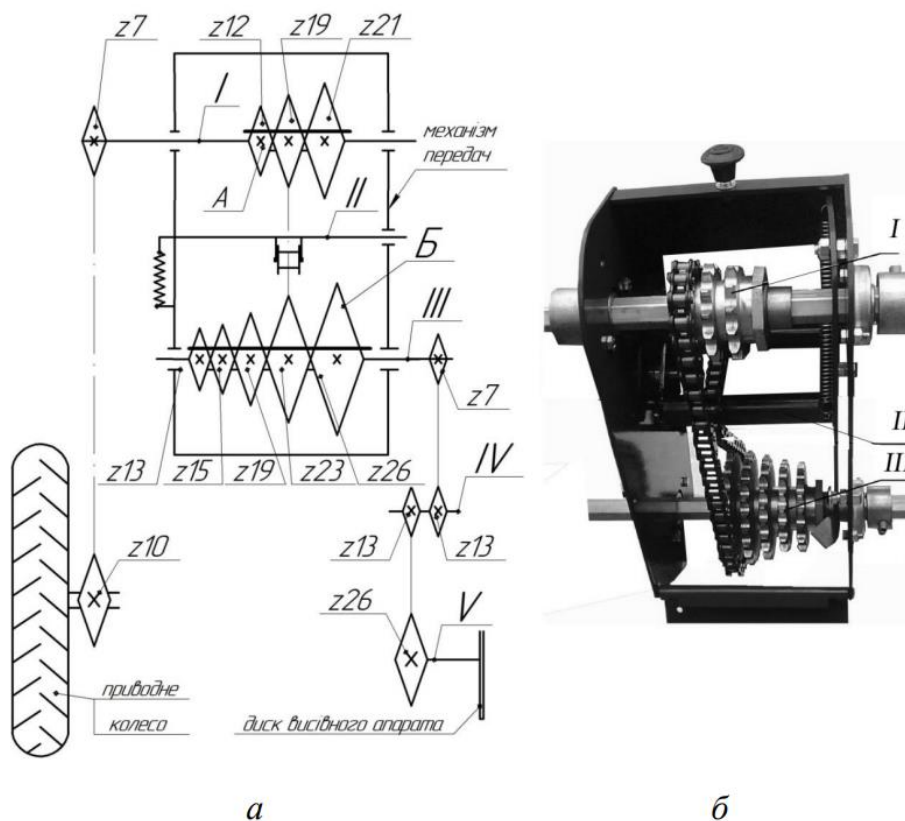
Коробка зміни передач СЗ-3,6А
